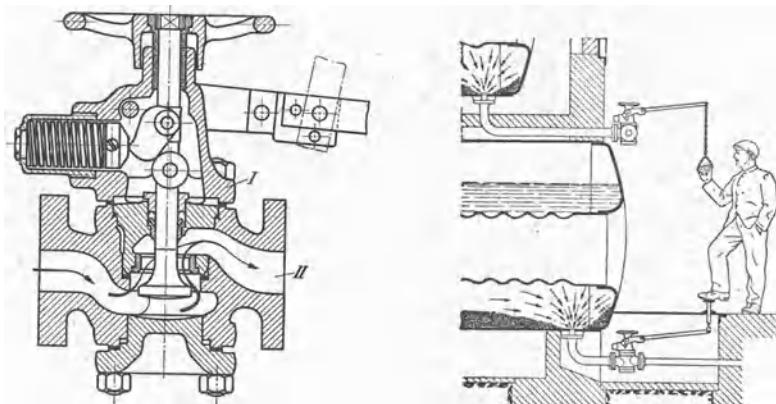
u. 161. Abschlämmpapparat von F. Gustav Gerdts, Bremen, geöffnet, viel im Gebrauch, hat eine sehr große Schließkraft, die dichten und schnellen Abschluß des gehärteten Ventilegels gewährleistet, kleinen lichten Durchgang (30 oder 40 Millimeter), so daß die Strömungsgeschwindigkeit groß ist und feste Bestandteile fortreißt, eine Überlastungssicherung, die den Ablaufstufen gegen Bruch schützt, falls der Belastungshobel zu stark gehandhabt wird. Er wird auch so ausgeführt, daß die Herausnahme des Abschlämmp-Mechanismus bei vollem Betrieb möglich ist. Bei tagsüber öfterem Gebrauch genügen immer nur wenige Sekunden für das Abschlämmpen.
